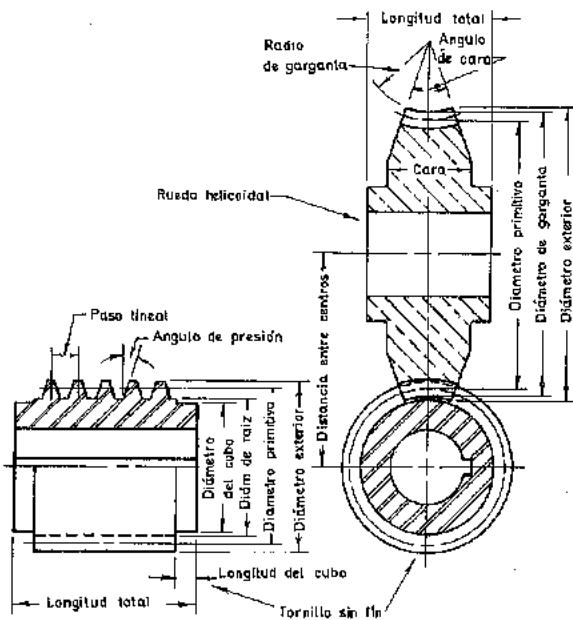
Partes y términos de los engranajes de tornillo sin fin.
